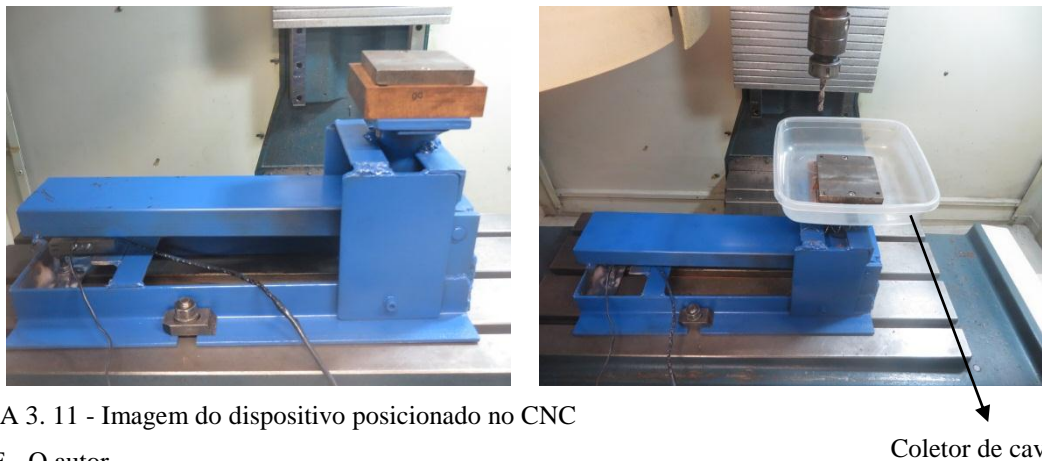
11 - Imagem do dispositivo posicionado no CNC
